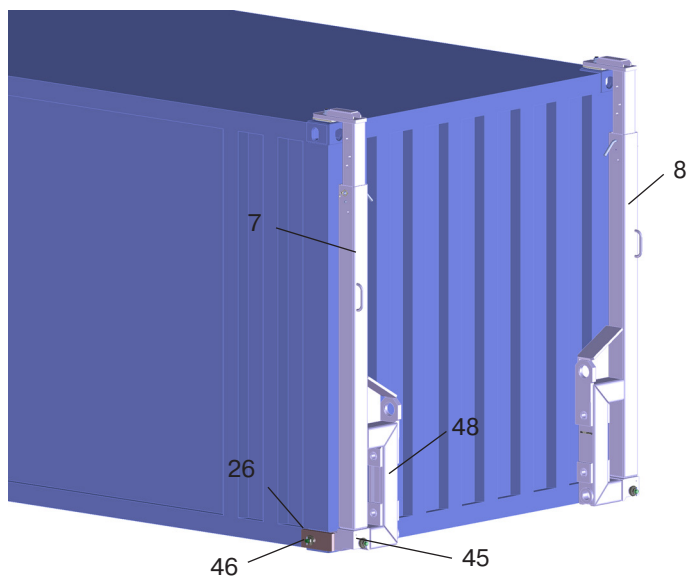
Rollbetrieb ‚Schmalspur‘ / Ladebetrieb ‚Schräge Rampe‘
